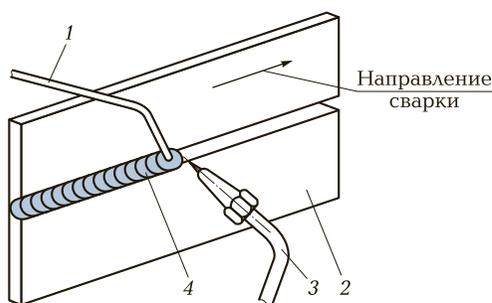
Схема сварки горизонтального шва:
